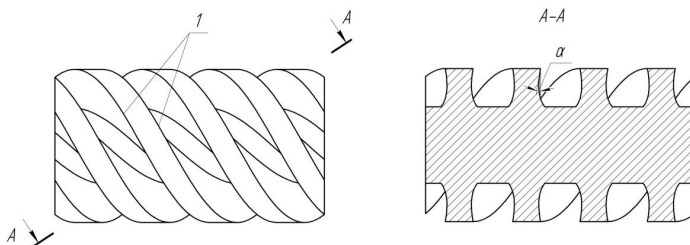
Конструкция инструмента червячного типа (1 – винтовые режущие кромки, α – задний угол).
